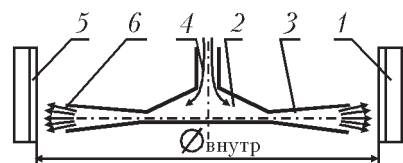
Схема устройства для нанесения покрытий на внутреннюю поверхность конструкций:
